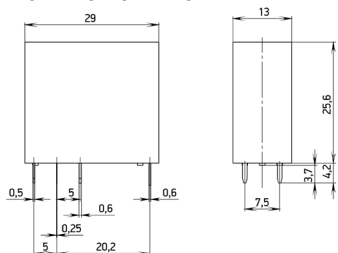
Габаритные, установочные, присоединительные размеры реле OptiRel G RP40-52 и OptiRel G RP40-61 с CO контактами
